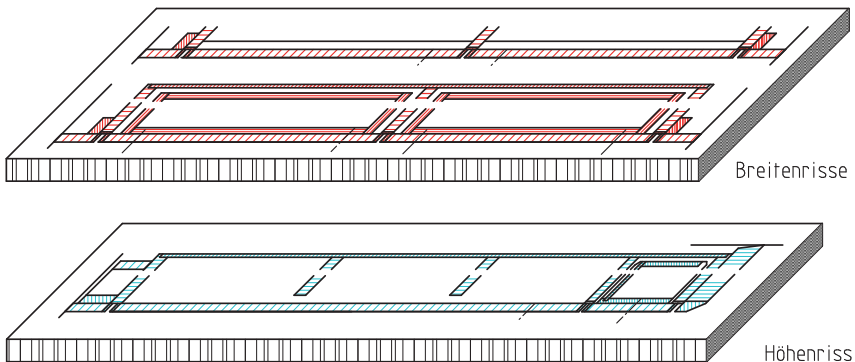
Aufriss (Fertigungsriß) mit Breitenriss und Höhenriss
